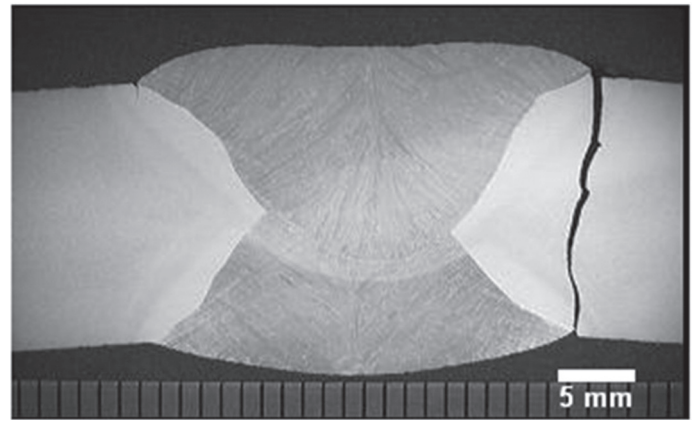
Trincas por fadiga adjacente a solda [8].
